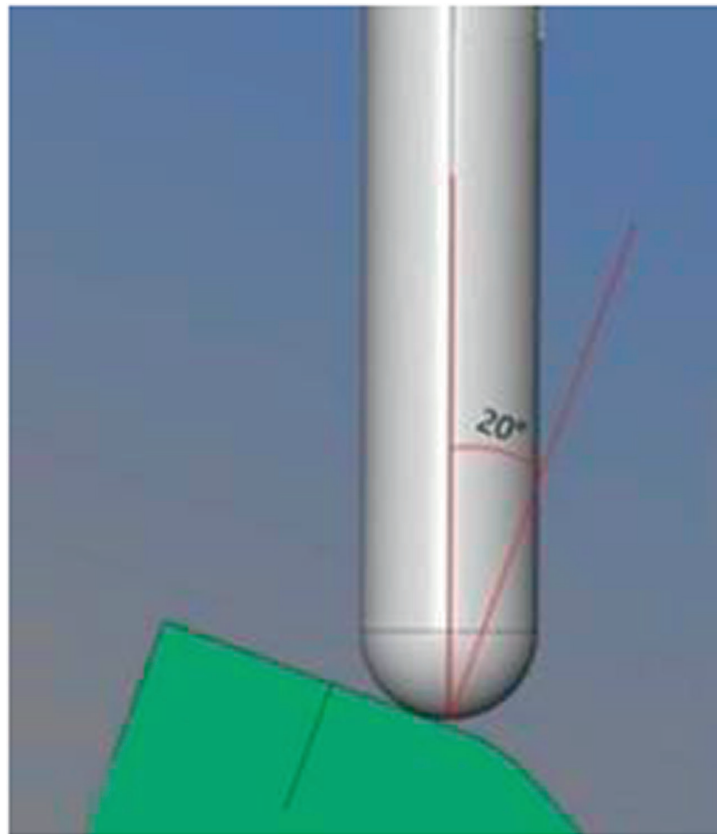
Inclinação entre fresa e peça durante usinagem do Platô.
